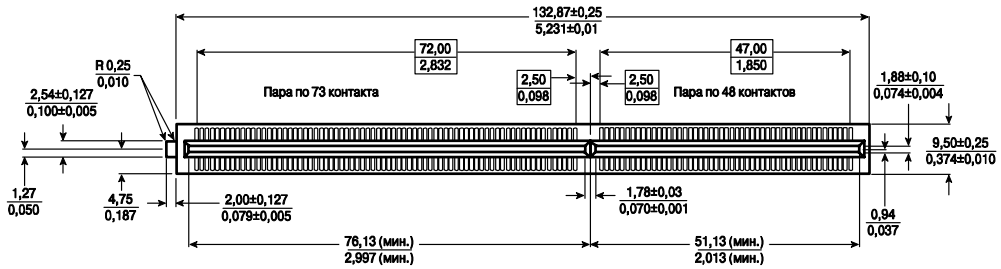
Размеры разъема Slot 1 для процессора Pentium II
